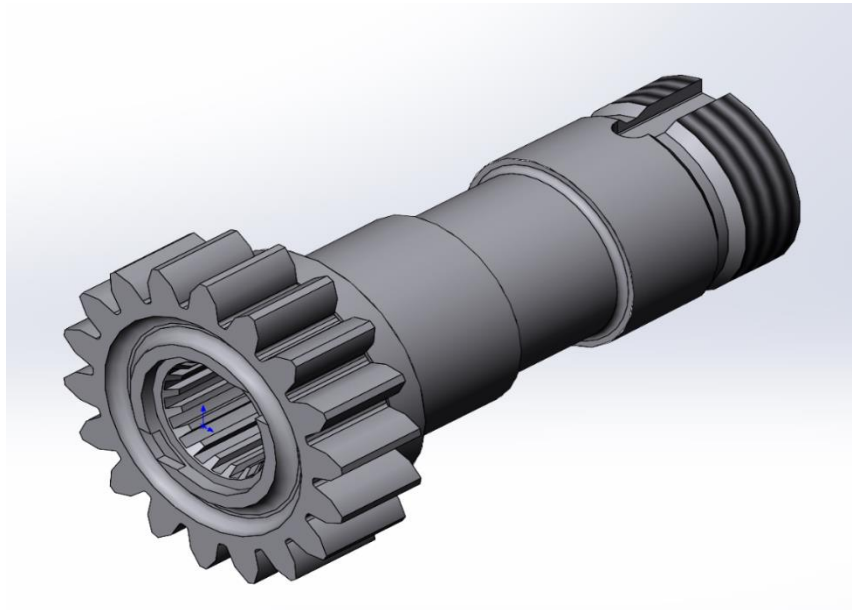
3D-модель деталі “Шестерня ”
